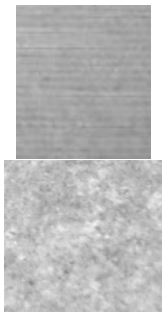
Циліндрична поверхня поршня з АЛ25 до і після корундування
